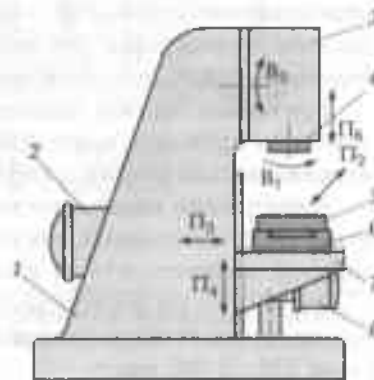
Компонировка консольного вертикально-фрезерного станка:
